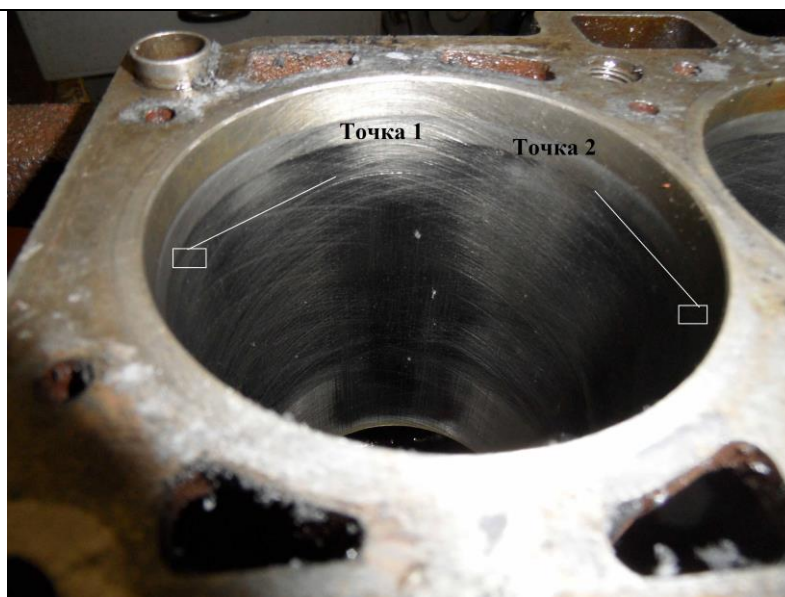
Точки замера шероховатостей на рабочей поверхности цилиндра
